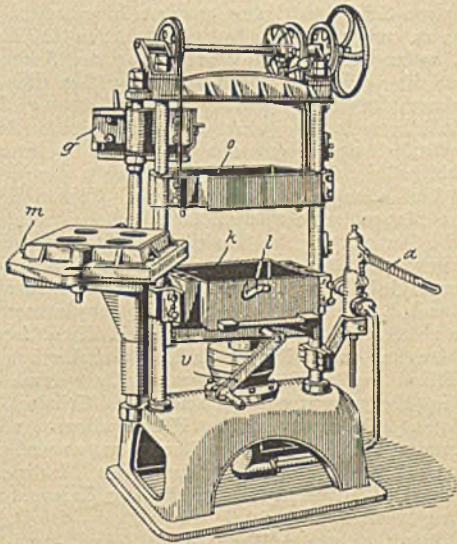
Hydraulische Formmaschine für kastenlosen Guß.
